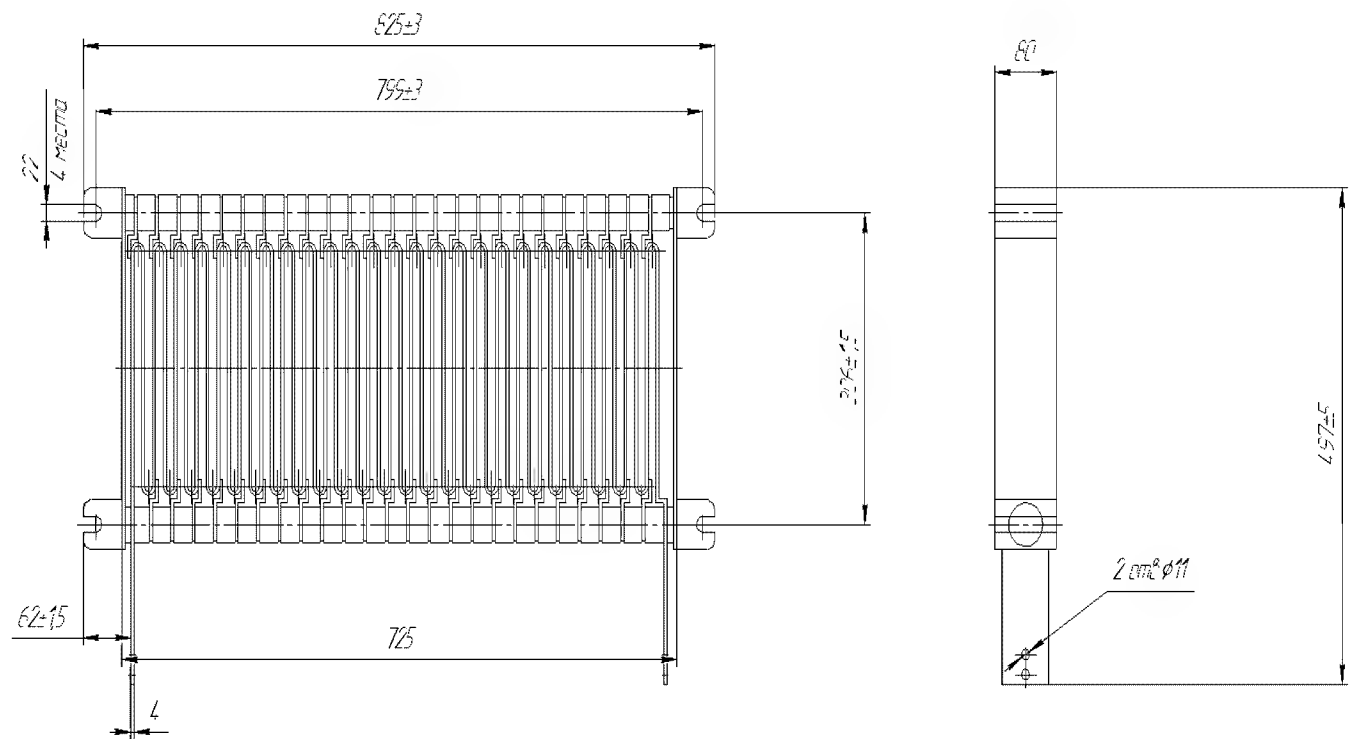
Габаритные размеры резистора типа РЛТ.
